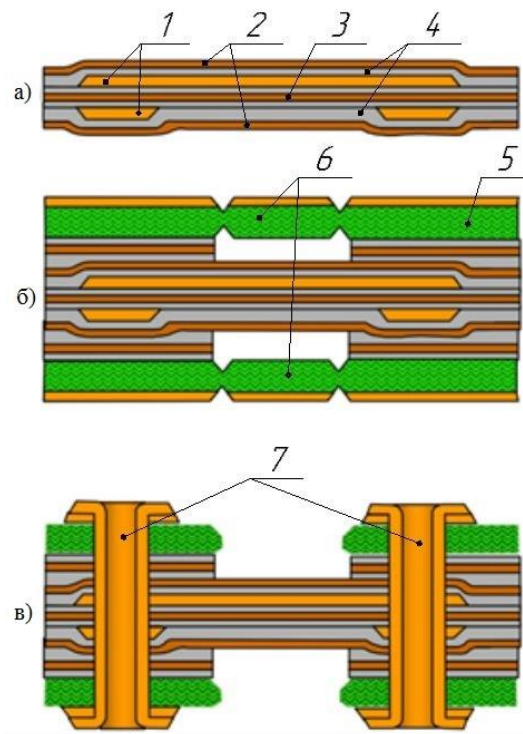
Процес виготовлення ГЖДП: а) Виготовлення гнучкої частини; б) ГЖДП після пресування;
